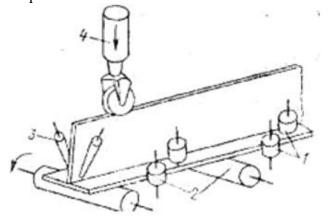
Схема работы станка для сварки тавровых балок СТС-2.
